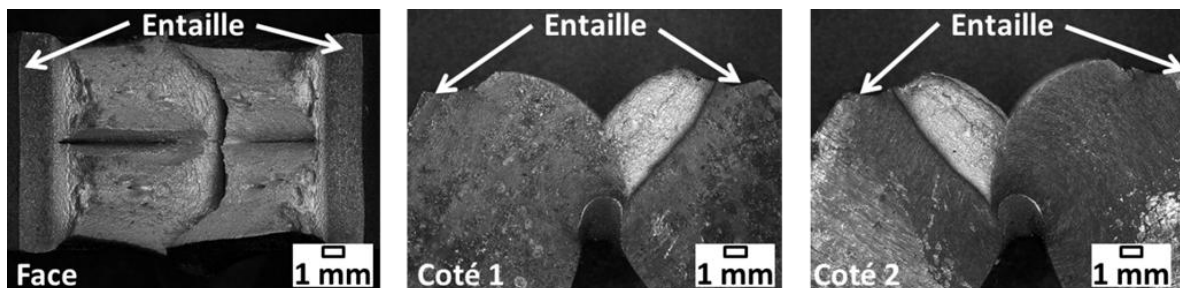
Fractographies d'une éprouvette de métal de base après essai Charpy
